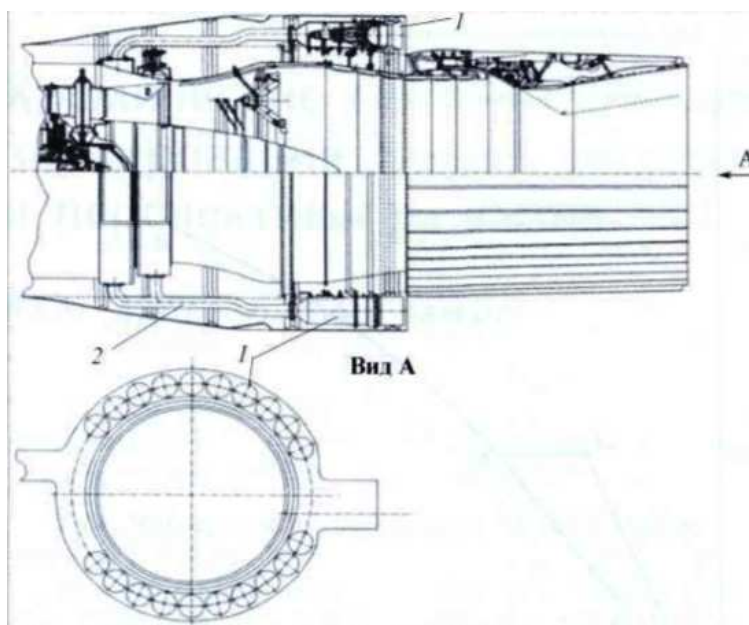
Схема размещения ПуДФК на корпусе форсажной камеры сгорания двигателя АЛ-31Ф: 1 - ПуДФК; 2 - патрубок подвода воздуха из наружного контура двигателя
